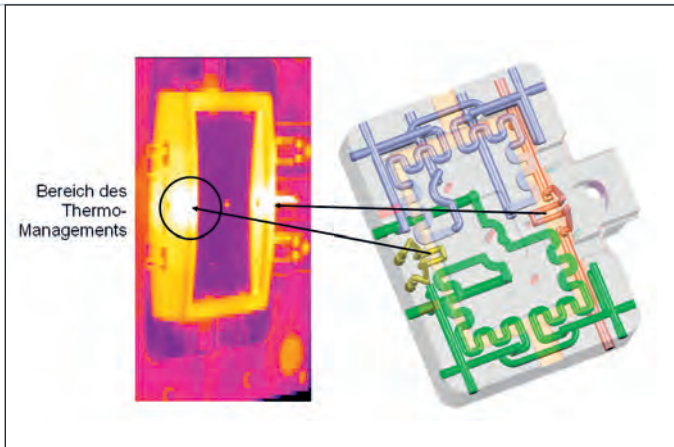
Infrarot-Aufnahme des Werkzeugeinsatzes für Thermo-Management
